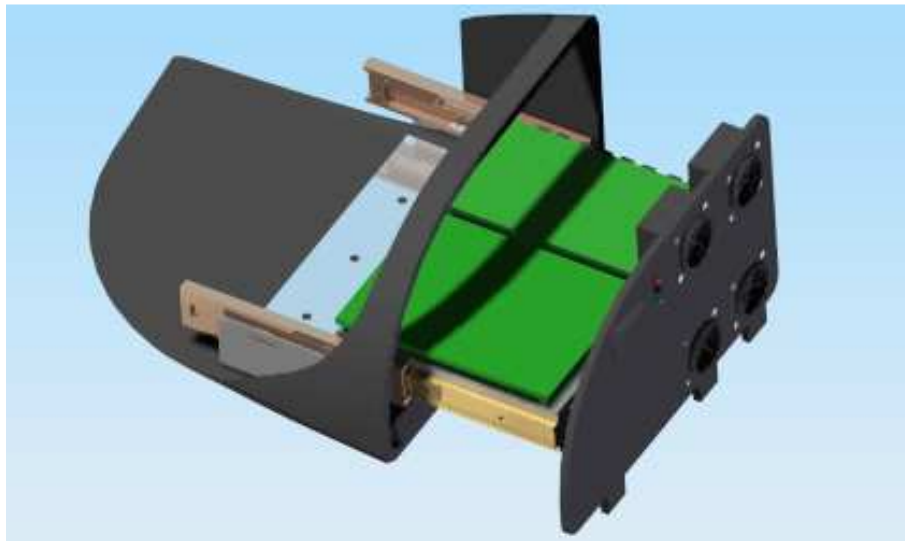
Tapa unida al elemento deslizante y cierre superior. Vista dimétrica
